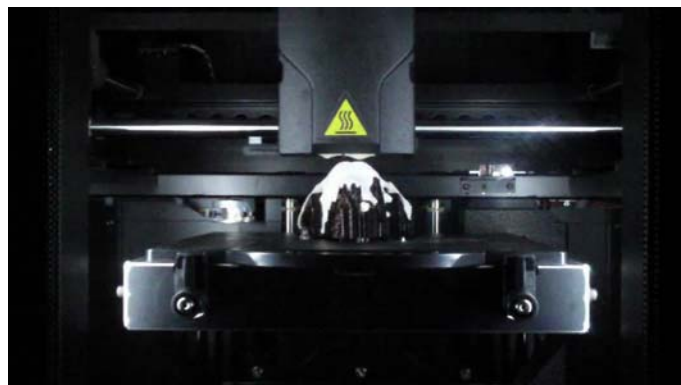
Cabezal y boquillas de la Impresora 3D modelo Dimension bst 1200es
